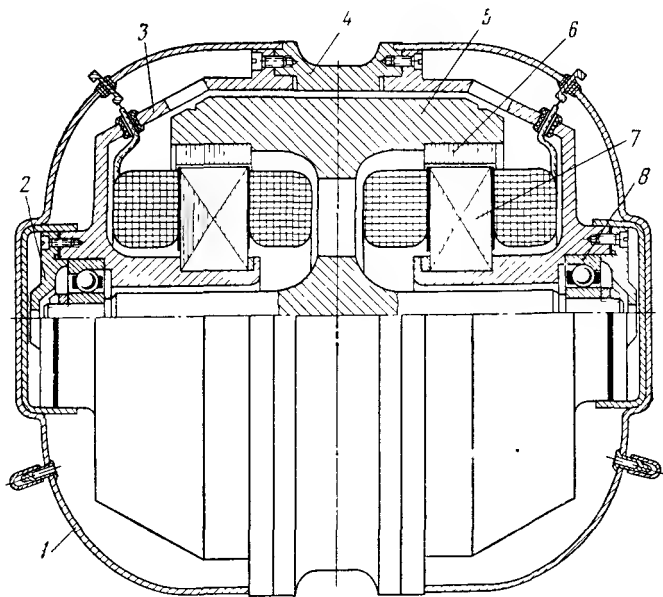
Двухстаторный гиродвигатель с электродвигателями обращенного исполнения:
